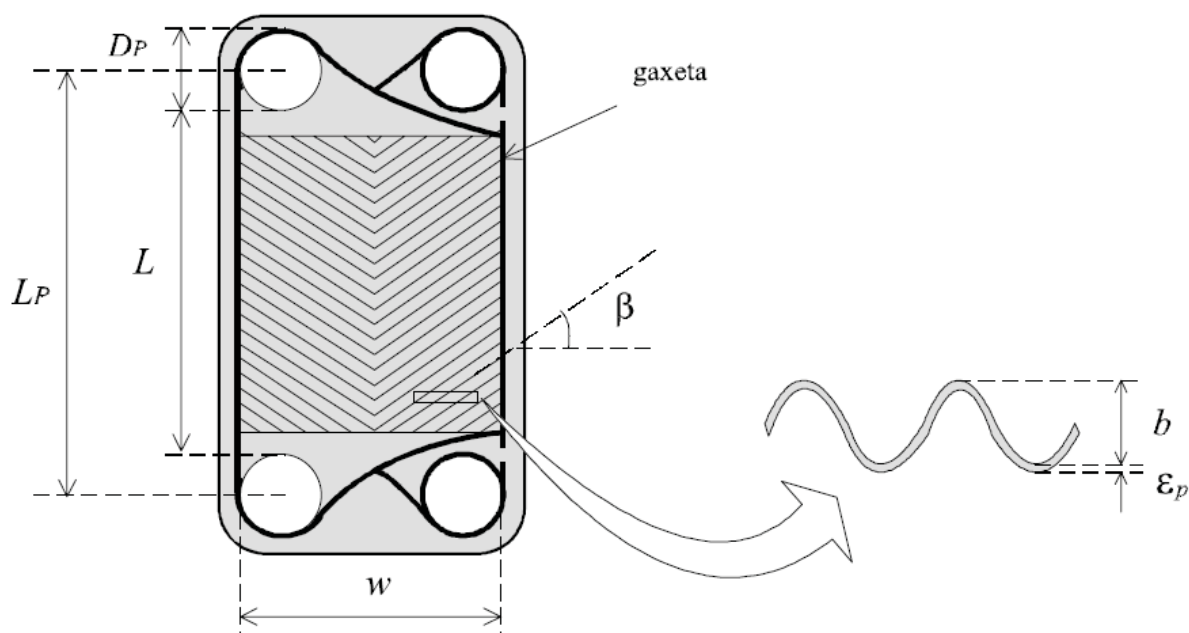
Principais dimensões de uma placa chevron (GUT, 2003).
